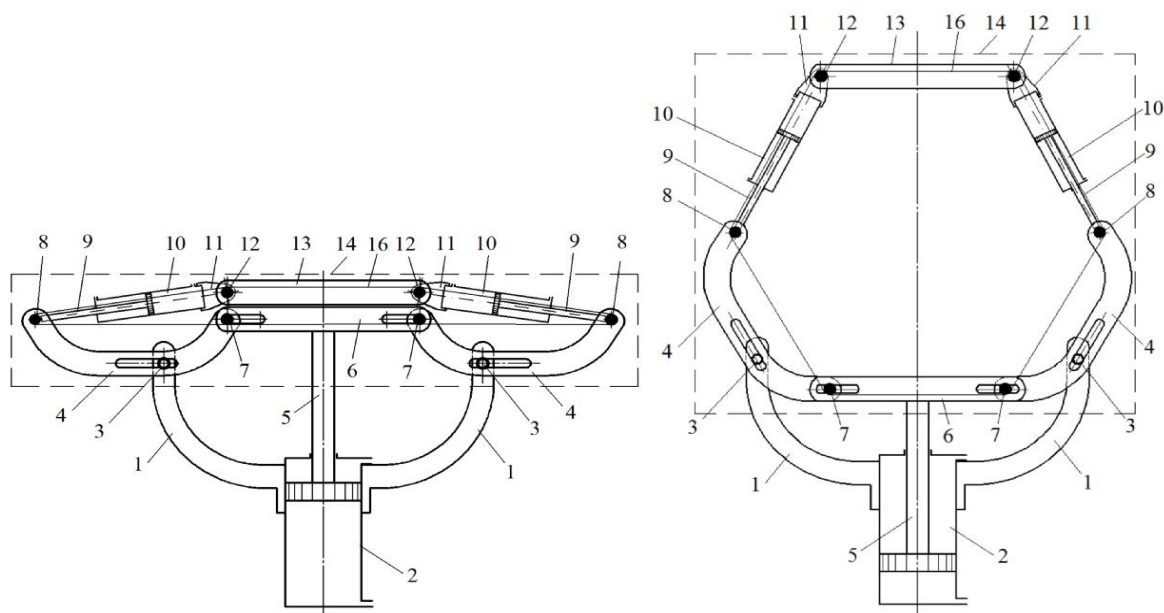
Рычажно-шарнирное захватное устройство в двух положениях:
